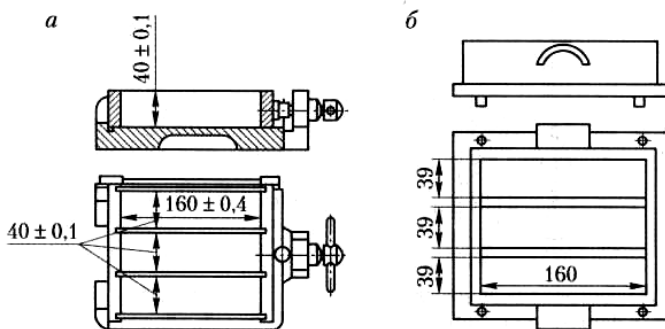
Форма для изготовления образцов-балочек (а) и насадка к ней с фиксаторами на наружных стенках (б)
